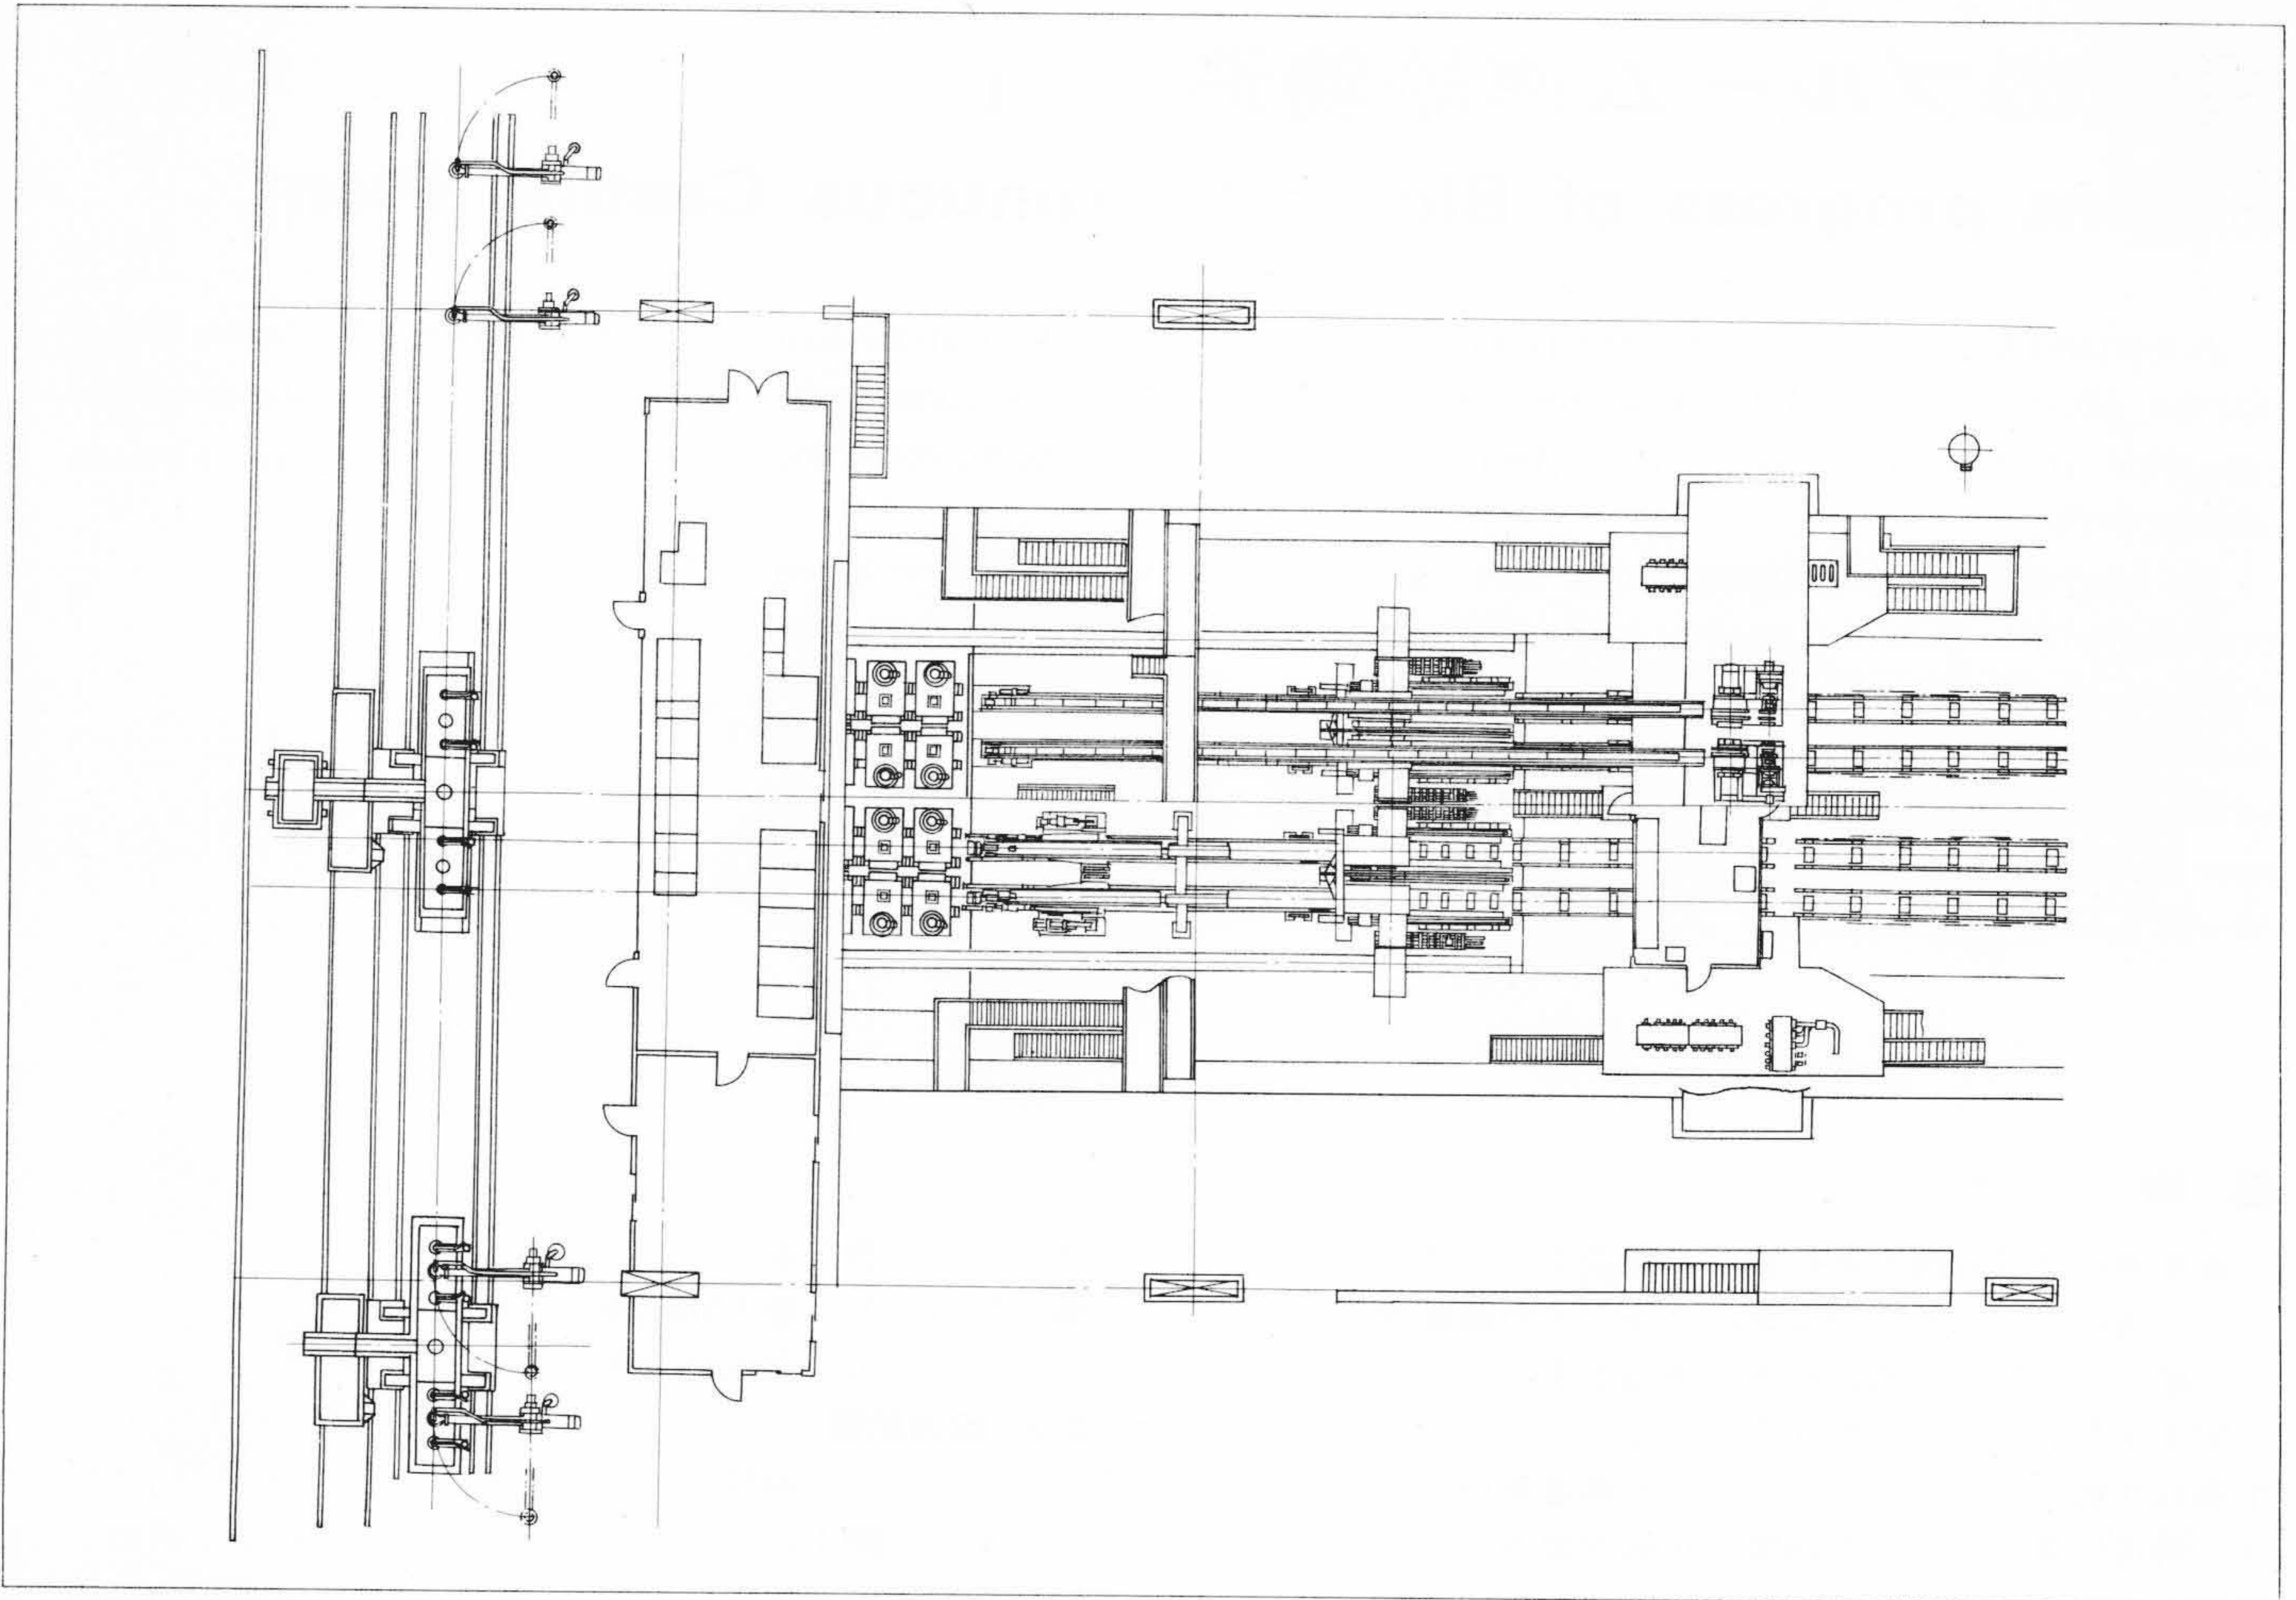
設備全体配置図 連続鋳造設備の平面配置を示したものである。
